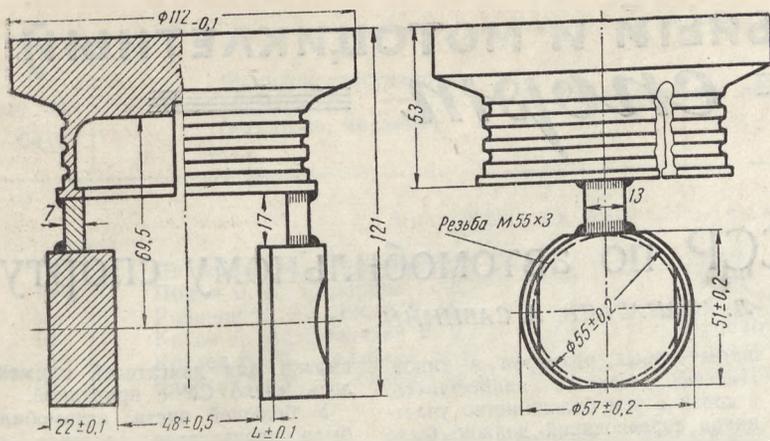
Заготовка стального днища в сборе с бобышками для поршневого пальца.
